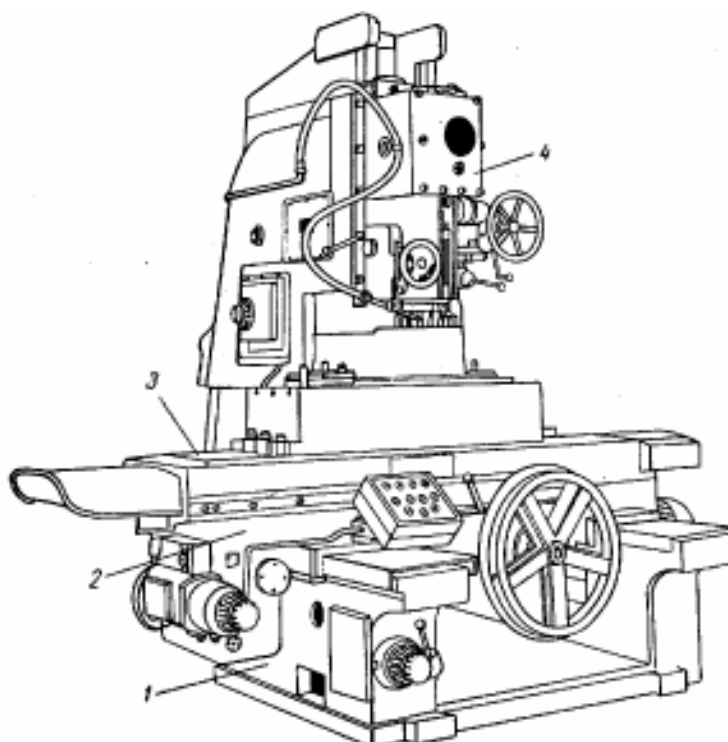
Бесконсольный вертикально-фрезерный станок ГФ
